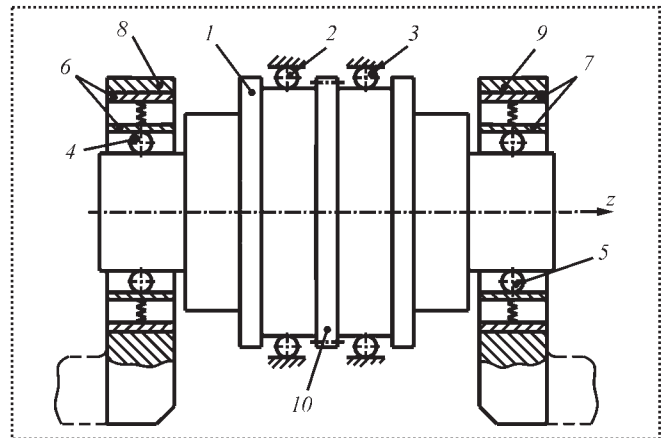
Схема конструкции жесткого ротора с упругоподвешенными массами
